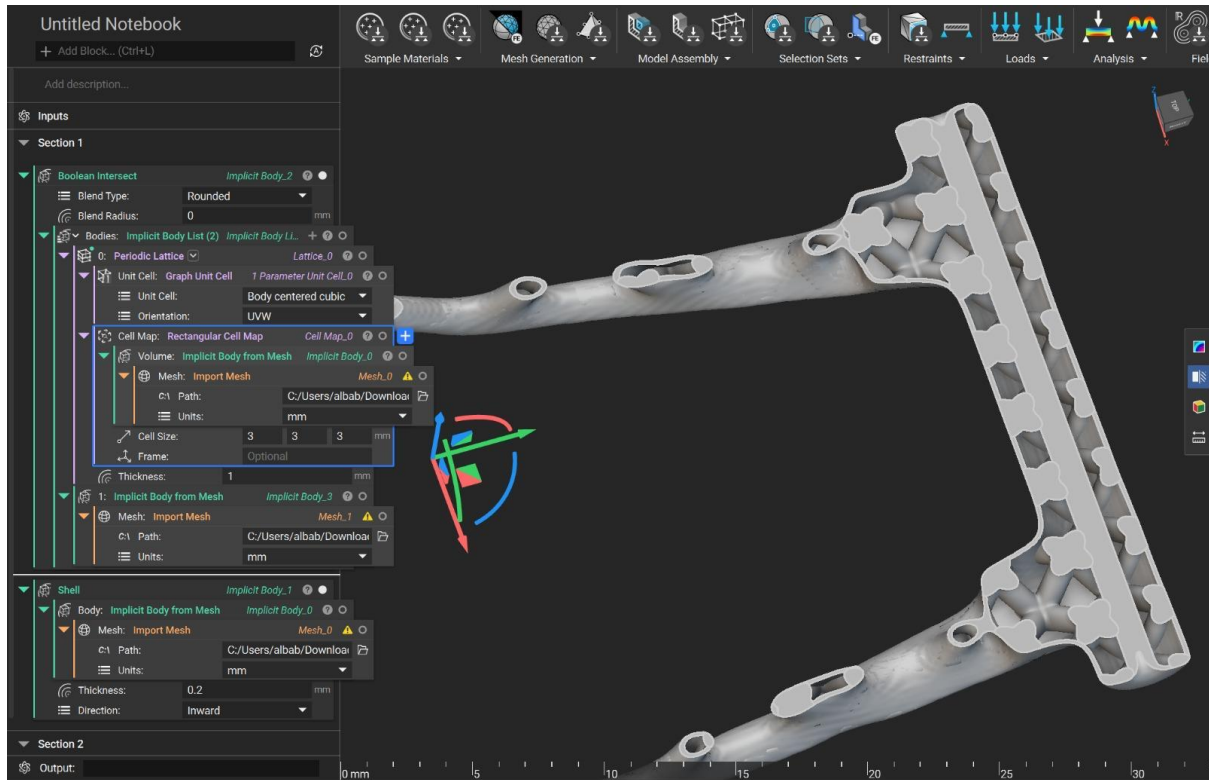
Estructura lattice Body centered cubic de 3mm
